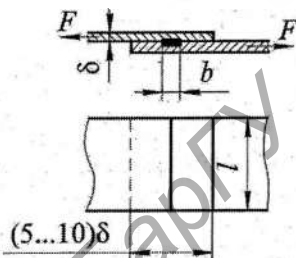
Соединение роликовой сваркой [3, с. 26]
